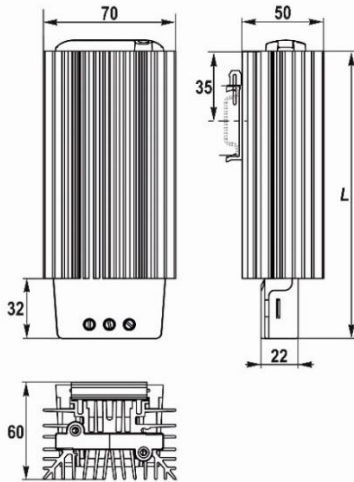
а – Общий вид и габаритные размеры нагревателей UNISPLIT 201FXXX
